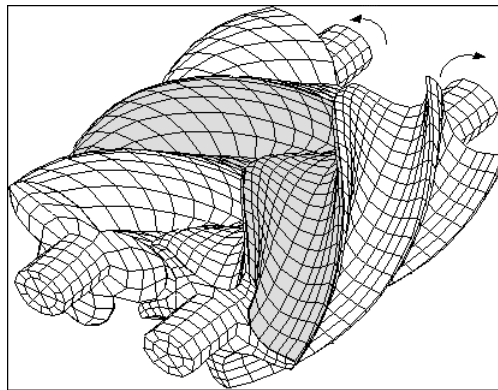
Expansionsvorgang beim Schraubenmotor /KAUDER 2001/
